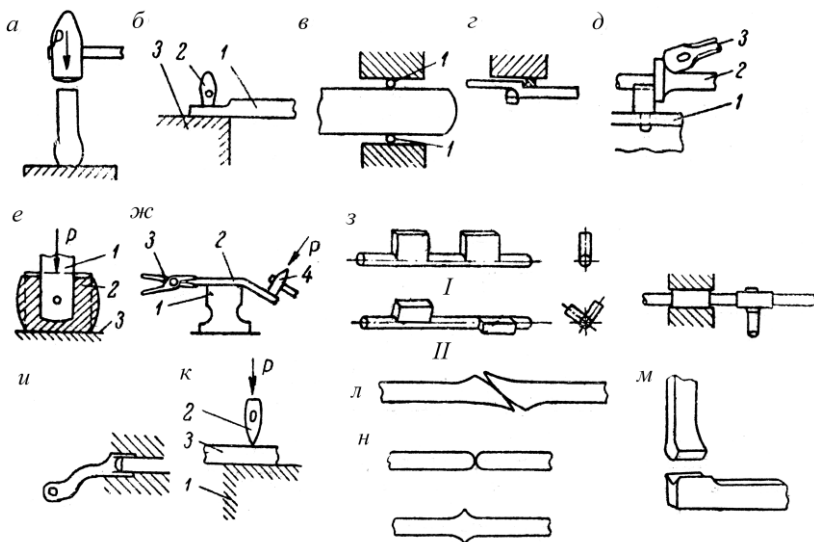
Операцииковки: а – высадка; б – вытяжка: 1 – обрабатываемая полоса; 2 – молот; 3 – наковальня; в – наметка: 1 – круглая раскатка; г – передача; д – приглаживание: 1 – наковальня; 2 – деталь; 3 – гладилка; е – прошивка: 1 – прошивень; 2 – обрабатываемый кусок металла; 3 – наковальня; ж – гибка: 1 – наковальня; 2 – полоса металла; 3 – клещи; 4 – молот; з – поковка двухколенчатого вала: I – до закручивания; II – после закручивания; и – закручивание; к – рубка: 1 – наковальня; 2 – зубило; 3 – обрабатываемая заготовка; л – кузнечная сварка внахлестку; м – кузнечная сварка в паз; н – кузнечная сварка встык
